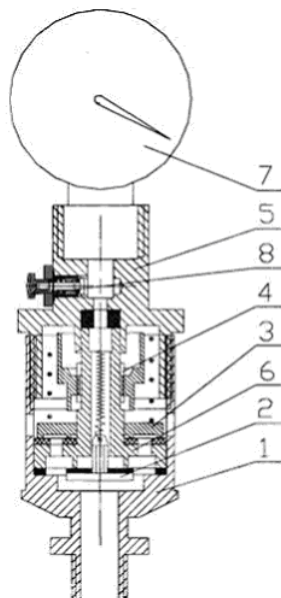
Прибор АГЦ-2. 1-нижняя часть корпуса; 2- запорный элемент; 3-подвижный элемент; 4-стопорная гайка; 5-верхняя часть корпуса; 6-корпус запорного элемента; 7-манометр разрежения; 8-стабилизирующий запорный элемент. [135]
